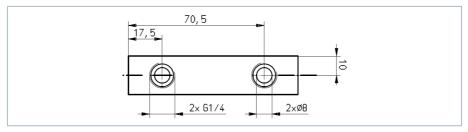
2 ELSA Steckverschraubungen (Push-In) in den Gewindebohrungen G 1/4 Zoll
